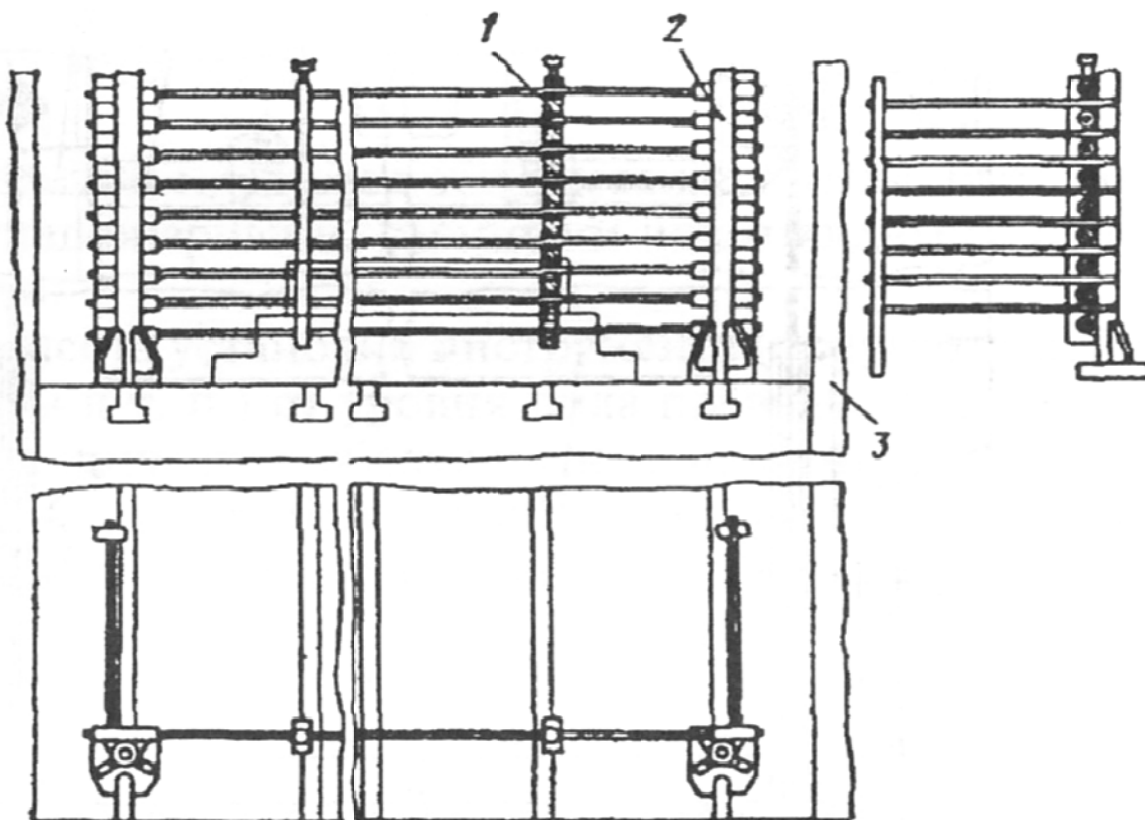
Универсальное неподвижное ограждение опасной зоны двухстоечных прессов:
